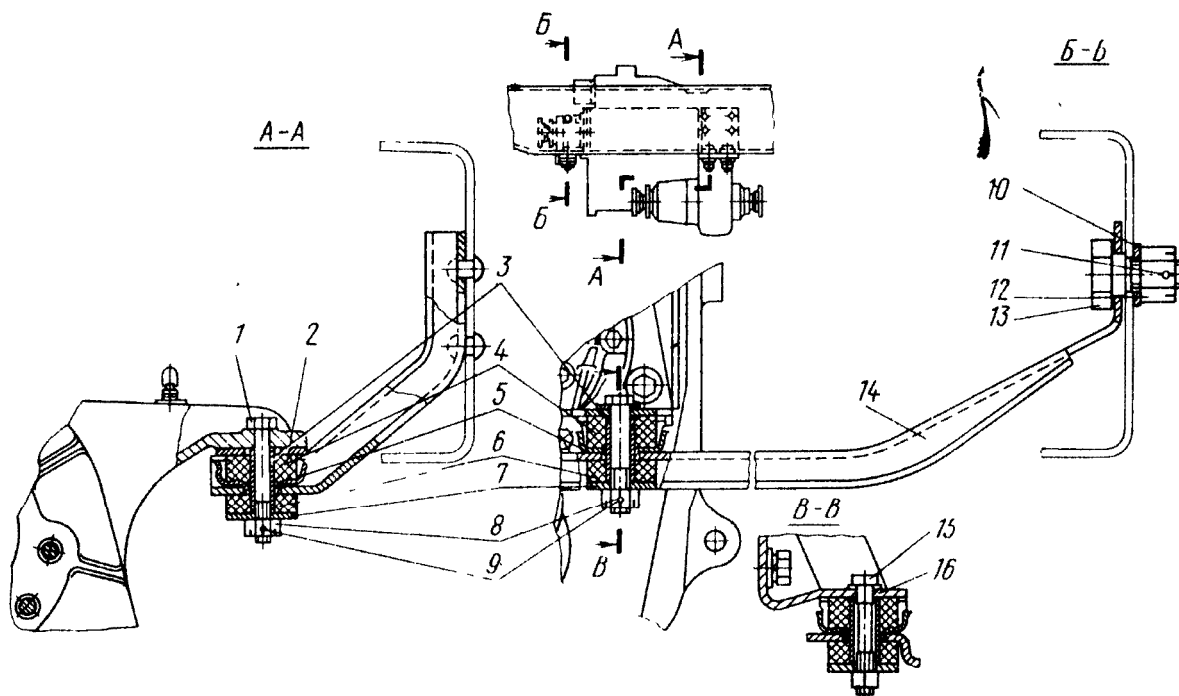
Подвеска коробки передач и раздаточной коробки:
